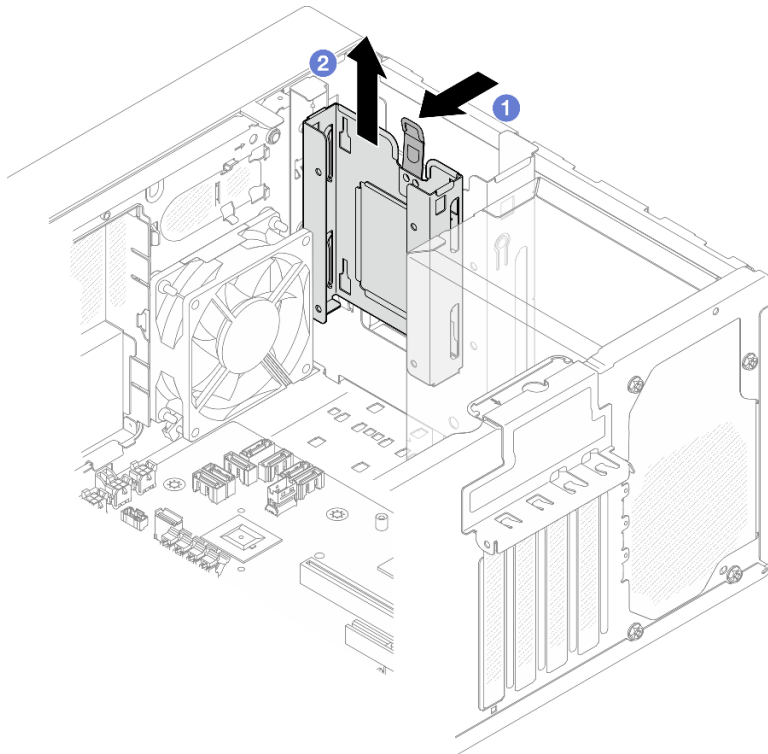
Entfernen der Laufwerkhalterung aus Laufwerkposition 1
